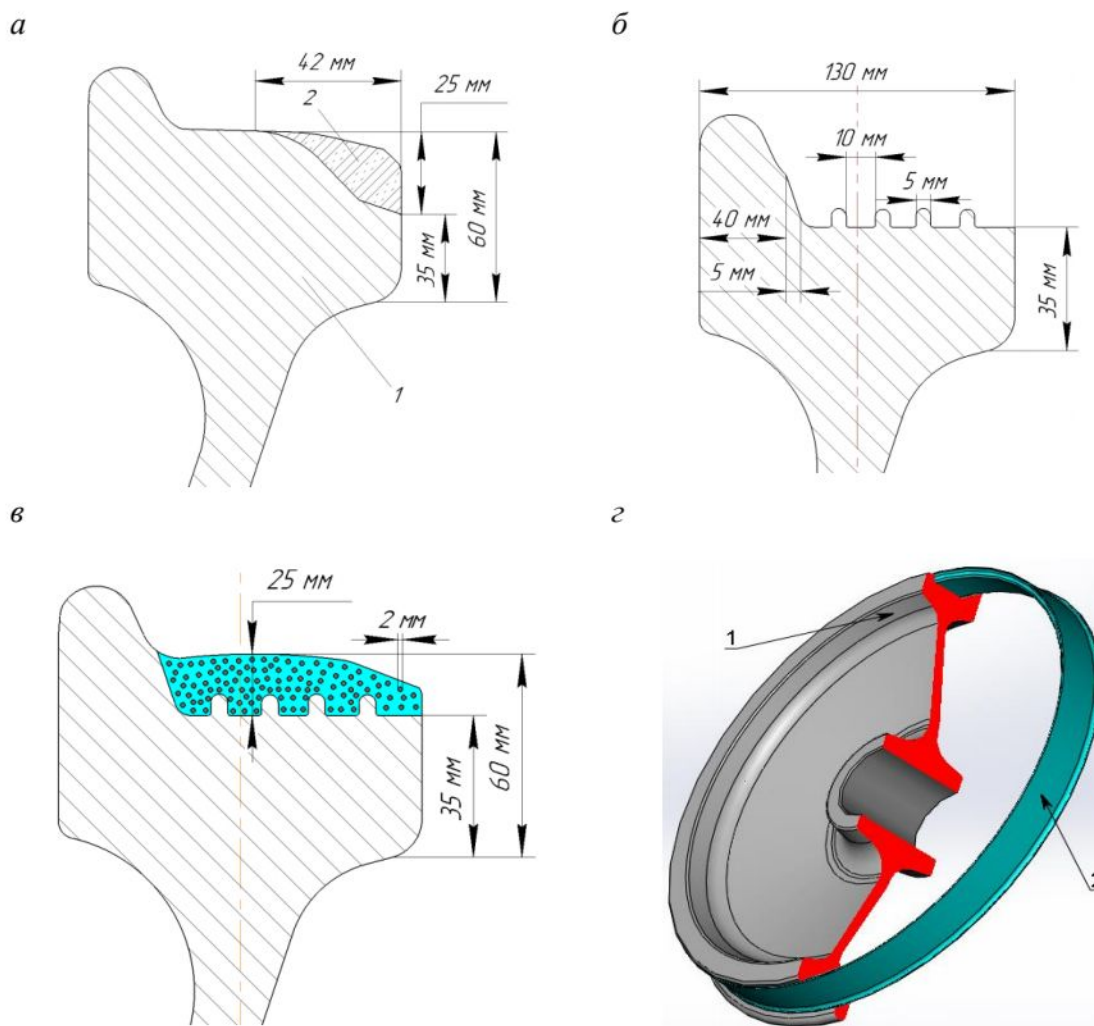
Схема обточки выемки на ободе колеса и формирования кольца из ПУ:
